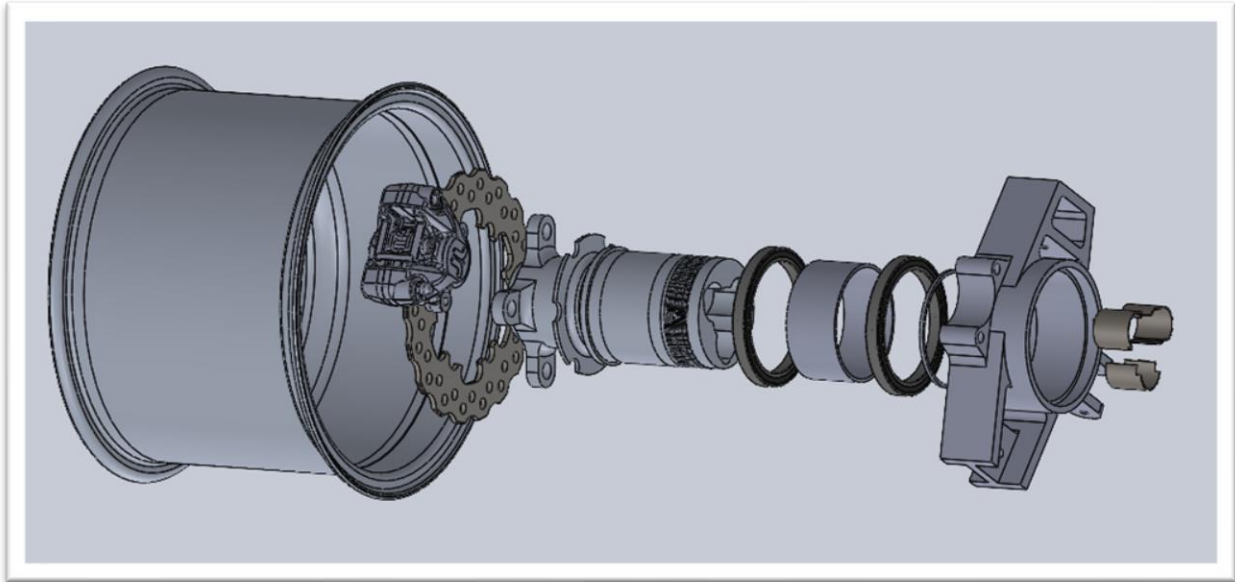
Vista explosionada del conjunto de las ruedas traseras (Vista 3D)
